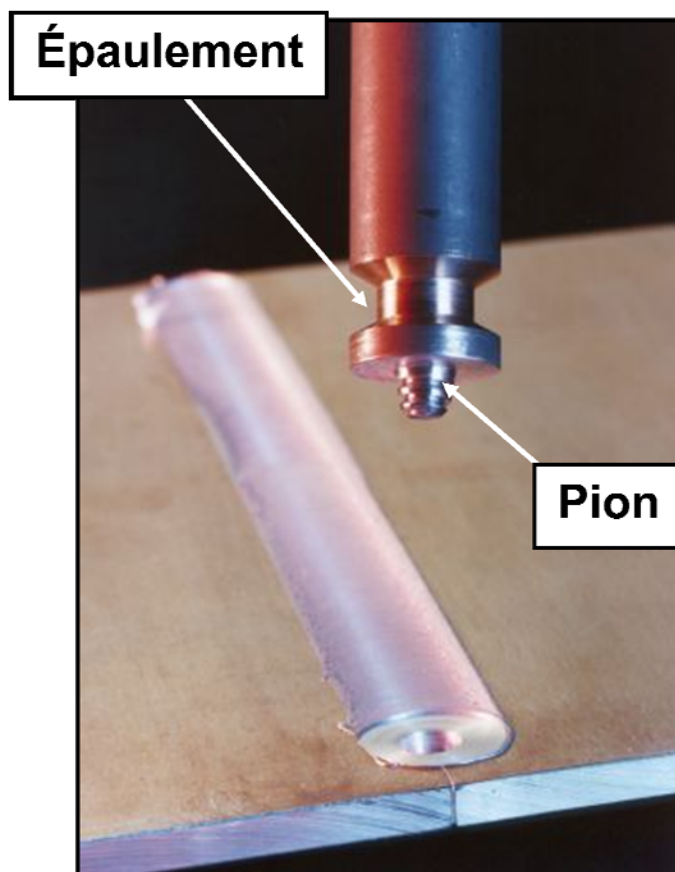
Principales composantes de l'outil de soudage et soudure bout à bout entre deux tôles.
